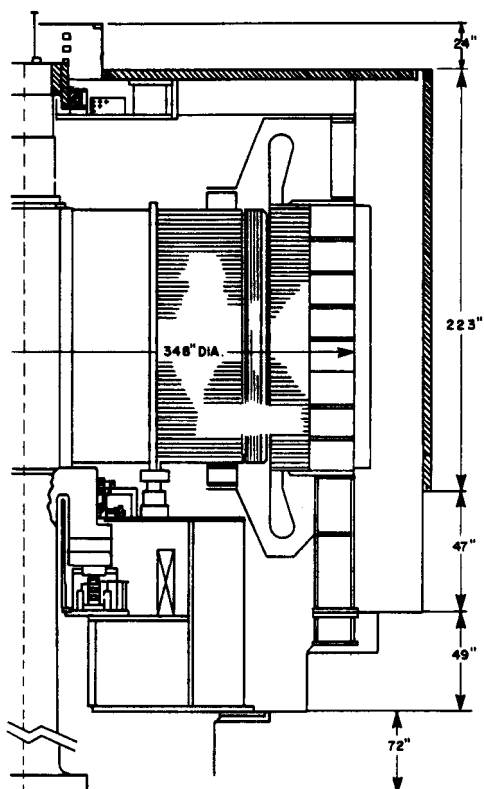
Desenho de um Motor-Alternador de eixo vertical
